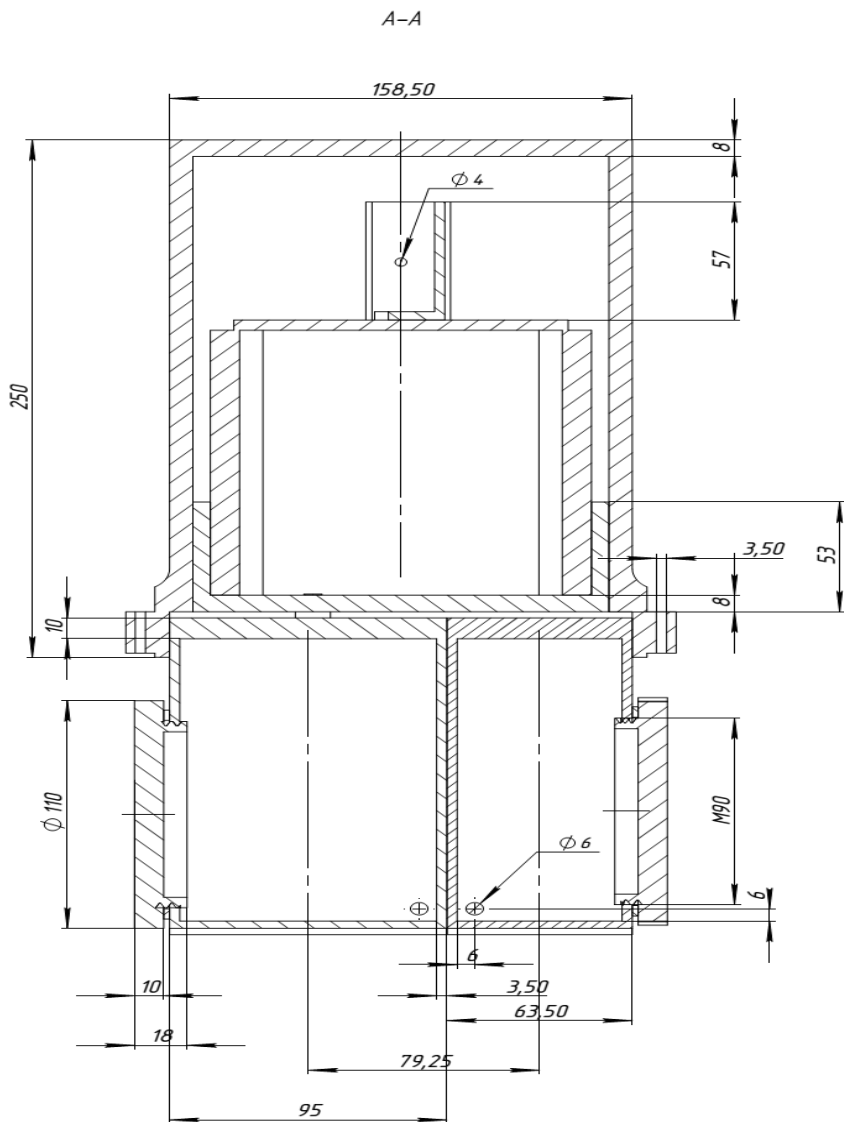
Корпус модуля (разрез спереди (сборка))
